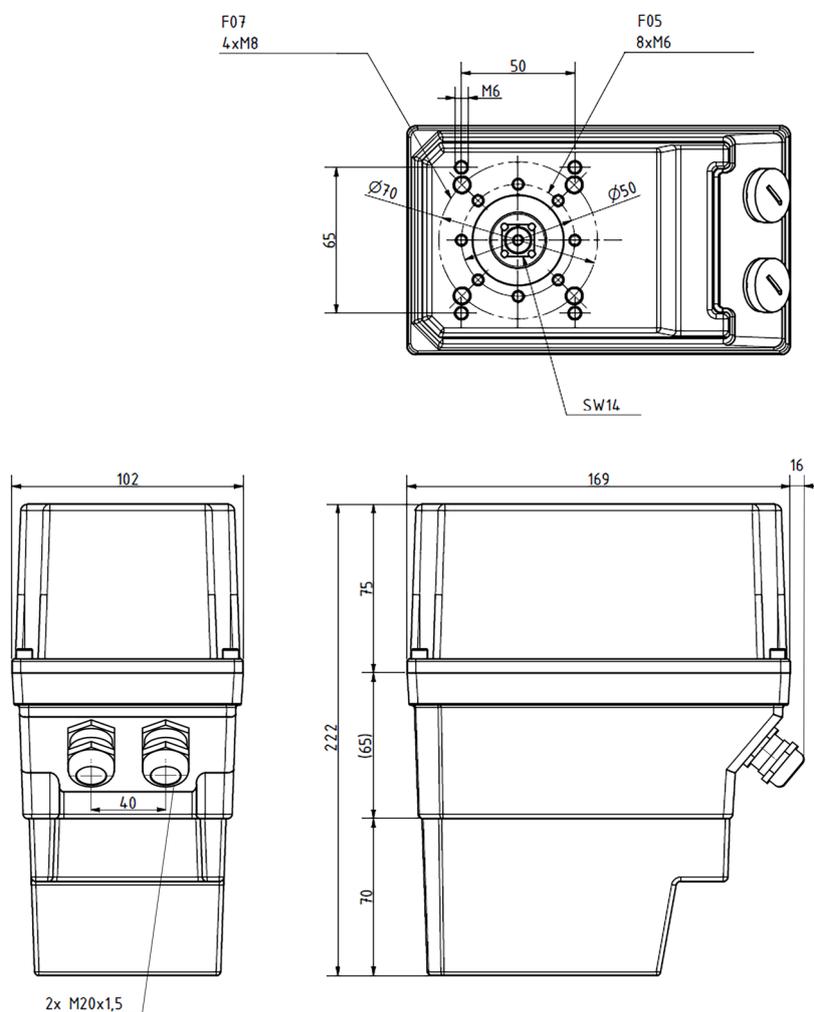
Plan coté du servomoteur 60 Nm avec entrée de câbles avec presse-étoupe (dimensions en mm)
